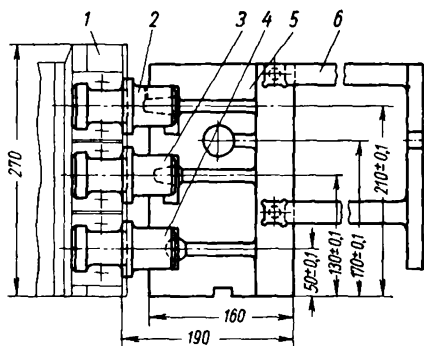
Высадочный штамп для поковки вида стержня с утолщением: 1 — блок пуансонов; 2 — наборный пуансон; 3, 4 — формовочные пуансоны; 5 — блок матриц; 6 — задний упор-рамка
